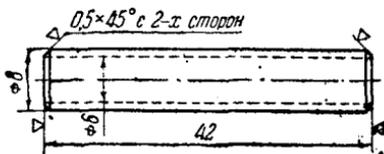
Дет. № 13-18. Трубка корпуса вентиля бензинового бака
